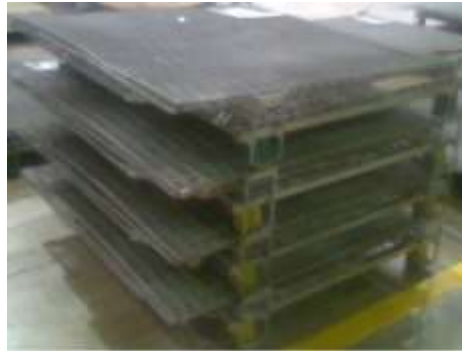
CESTAS METÁLICAS PLEGADAS
